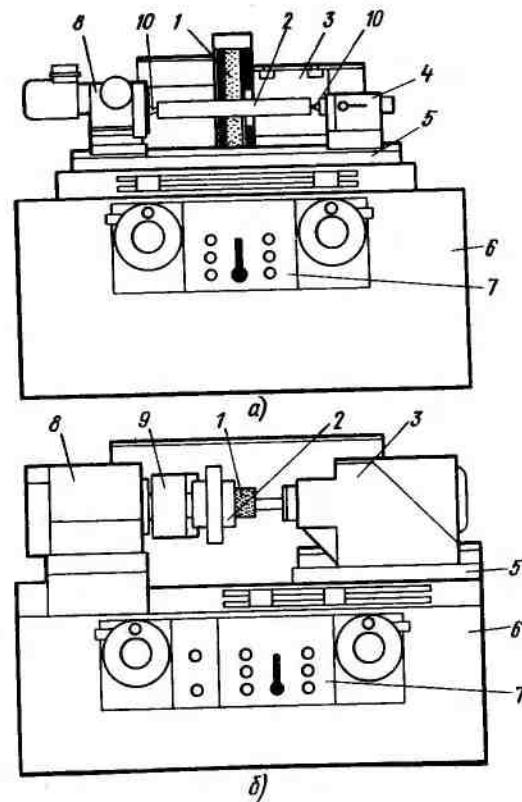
Основные узлы круглошлифовального (а) и внутришлифовального (б) станка
